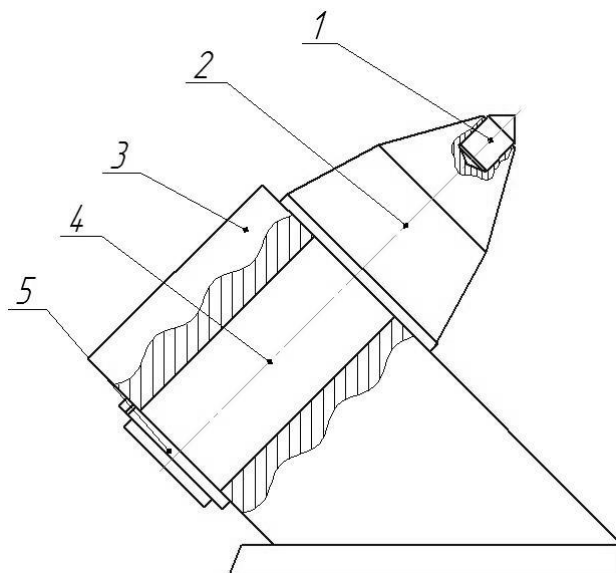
Тангенциальный поворотный резец новой конструкции в резцедержателе
